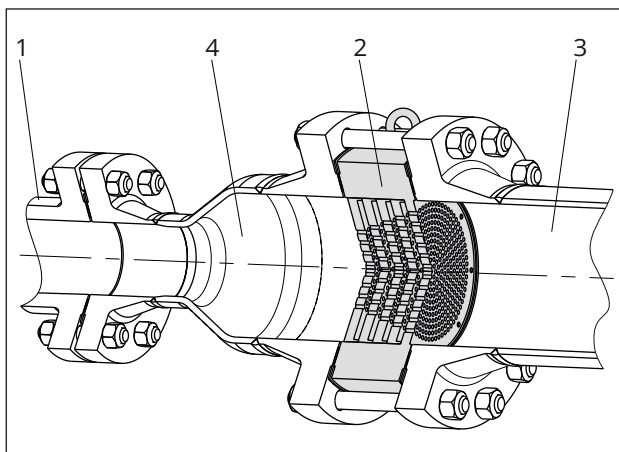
Тип 3381-4-5: пять дроссельных шайб установлены между расширением трубопровода и трубопроводом (конструкция «сэндвич»)
